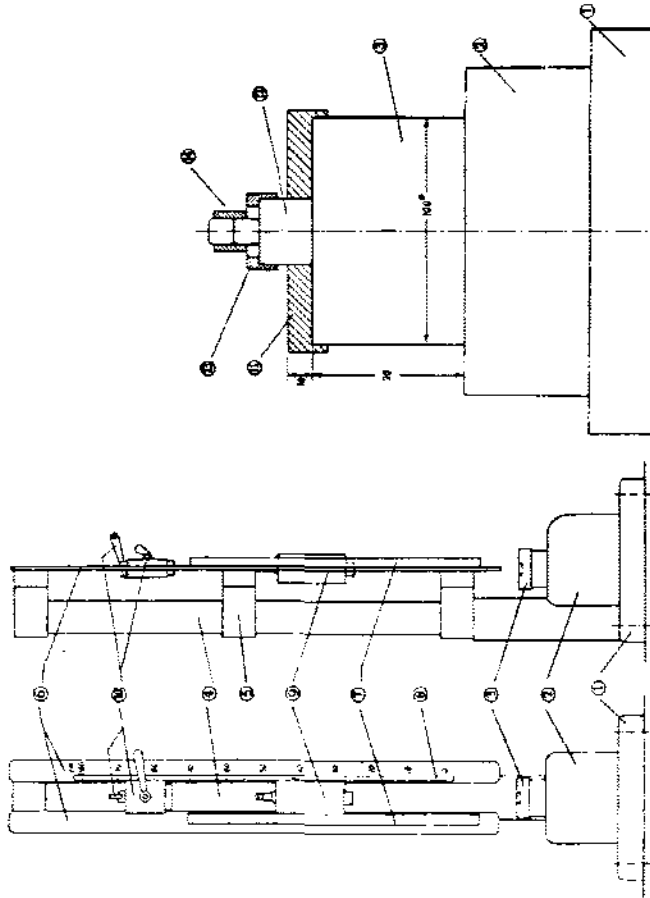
Maza de choque II, parte inferior. Dimensiones en mm.
